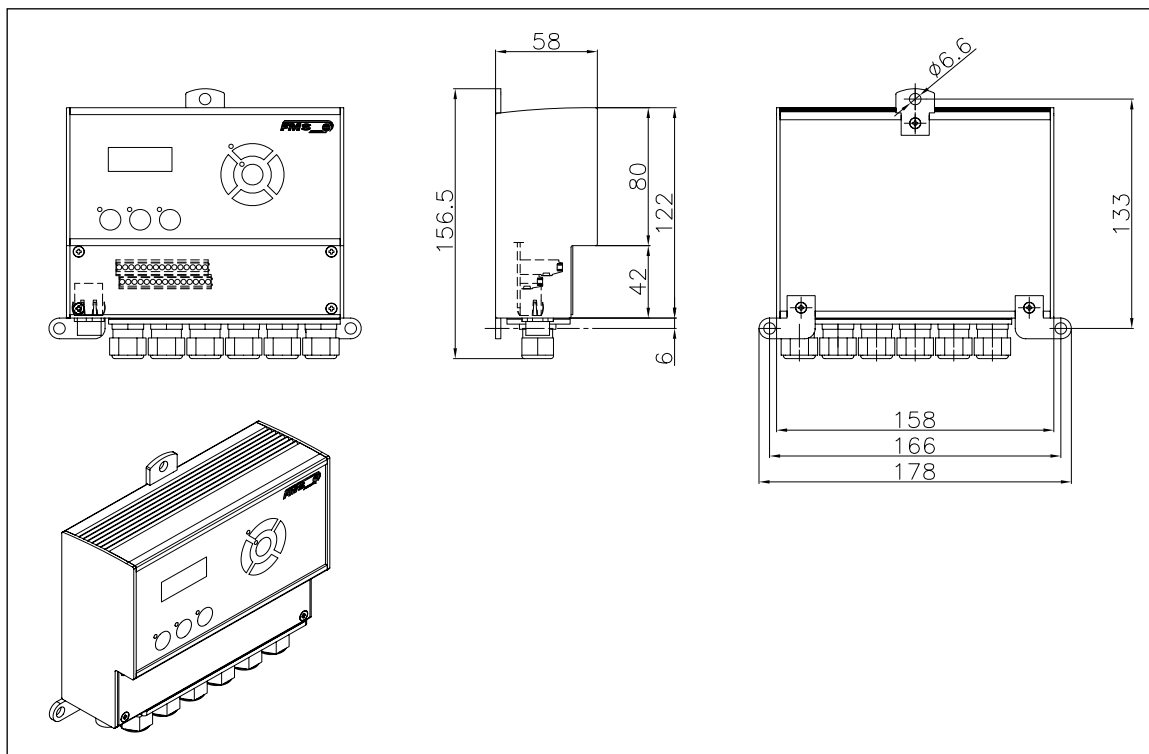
Aussenabmessungen CMGZ309.W Gehäuse für Wandmontage C309003
